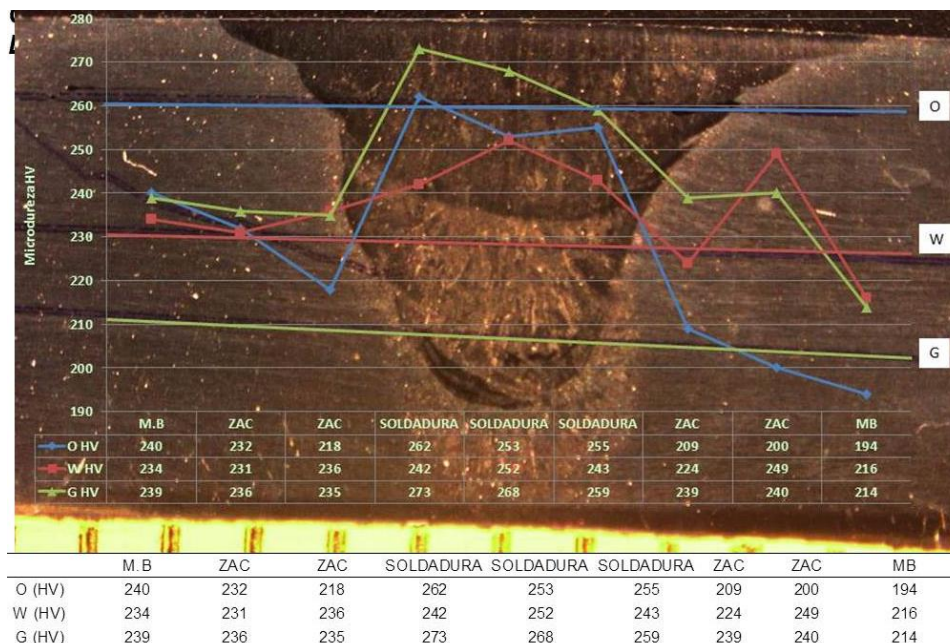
13 Perfil de dureza practicado a la unión soldada de AID 2205 mediante GTAW
